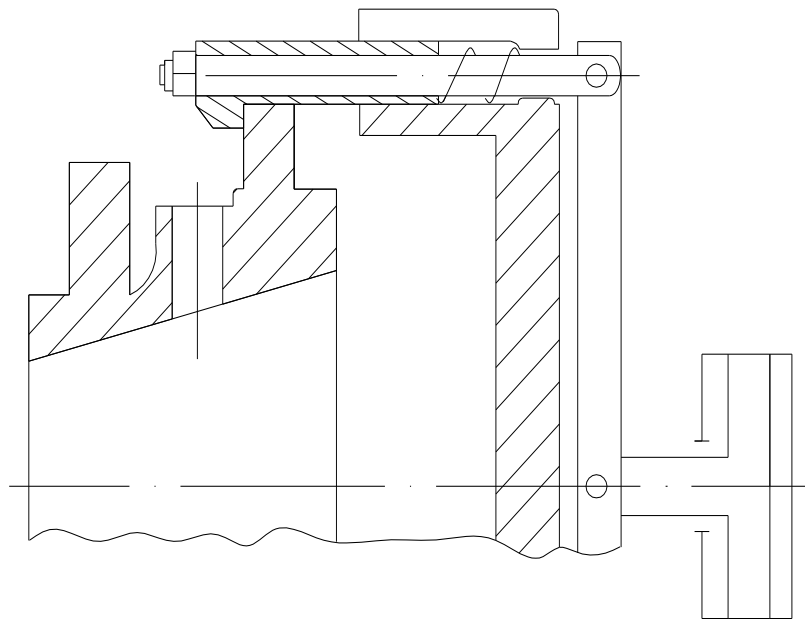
Схеми варіанту закріплення заготовок
